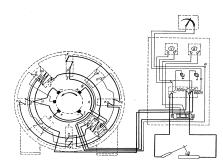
Схема соединений сварочного генератора типа СГП-3-VIII; вид со стороны коллектора
